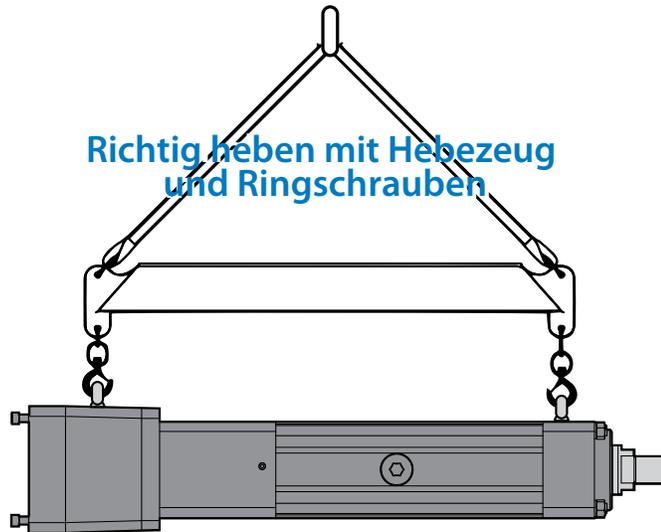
RSX richtig heben mit Hebezeug und Ringschrauben
